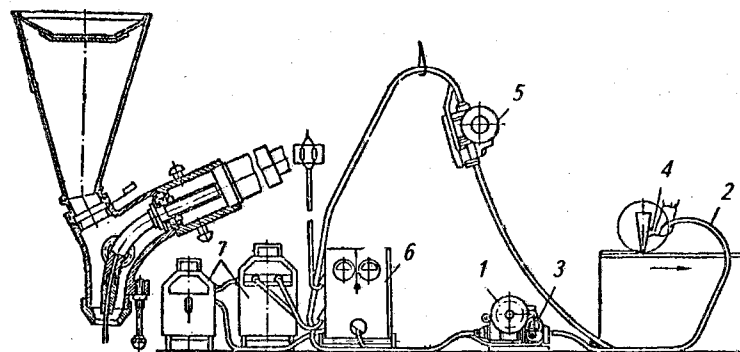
Схема поста полуавтоматической сварки под флюсом: 1 — кассета подающего механизма; 2 — гибкий шланг для подачи электродной проволоки и электрического тока; 3 — ролики подающего механизма; 4 — держатель; 5 — подающий механизм; 6 — аппаратный ящик с электрооборудованием полуавтомата; 7 — сварочный трансформатор
